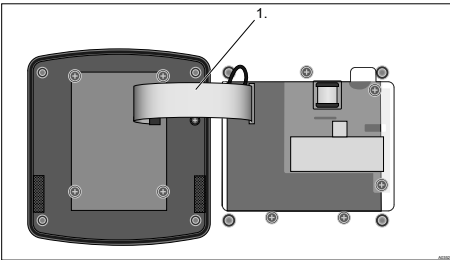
Flachbandkabel in Sockel stecken und verriegeln
